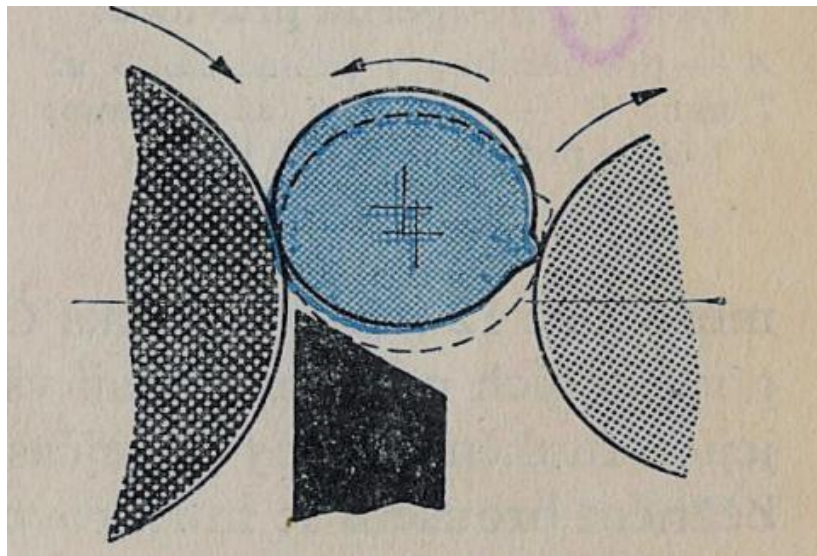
C – osa obrobku nad osami kotoučů [10]
